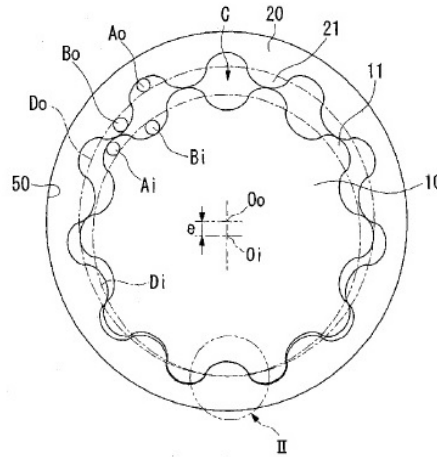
Conceito de bomba de engrenagens com caudal fixo [29].
